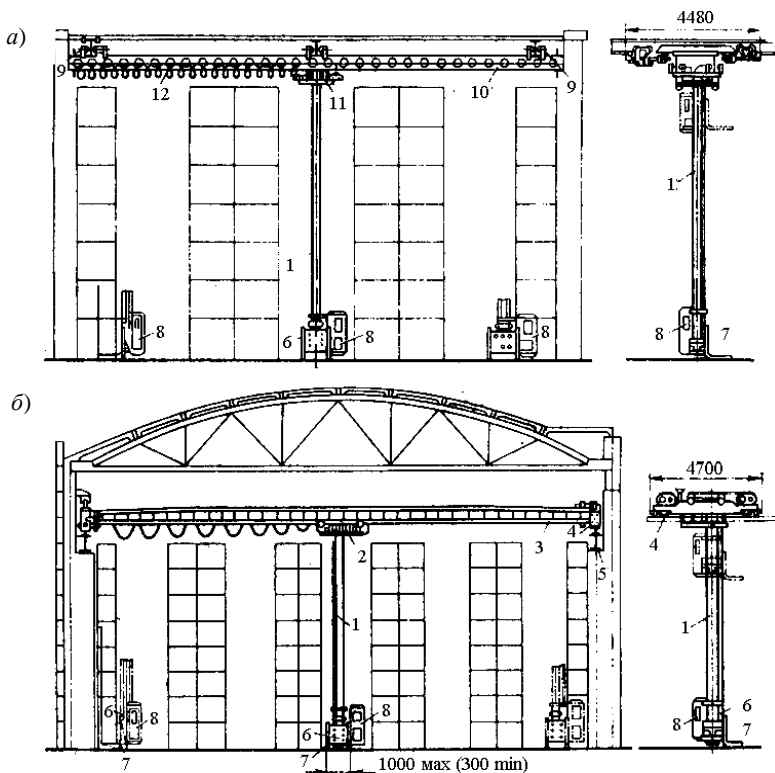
Мостовые краны-штабелеры с одной грузоподъемной колонной
